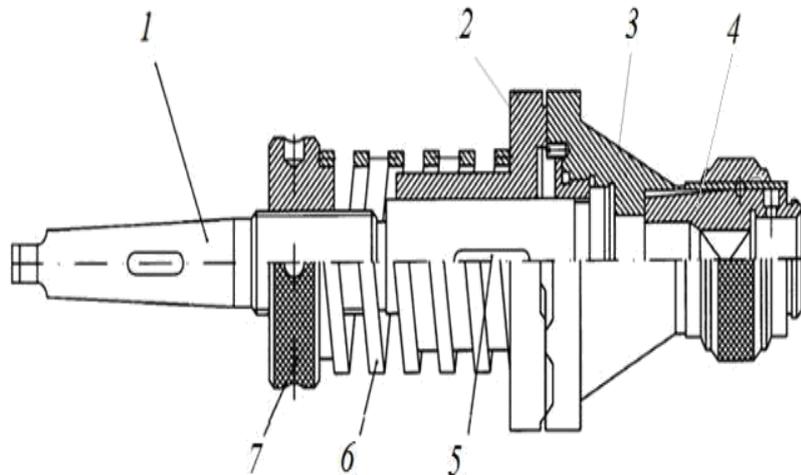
Патрон предохранительный, пружинно-кулачковый
